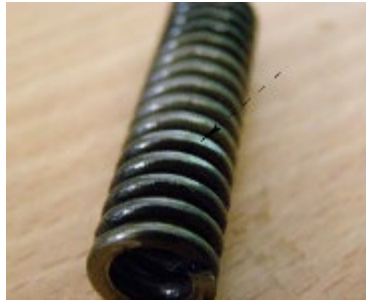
Пружина клапана (механічне зношення бокової поверхні)
